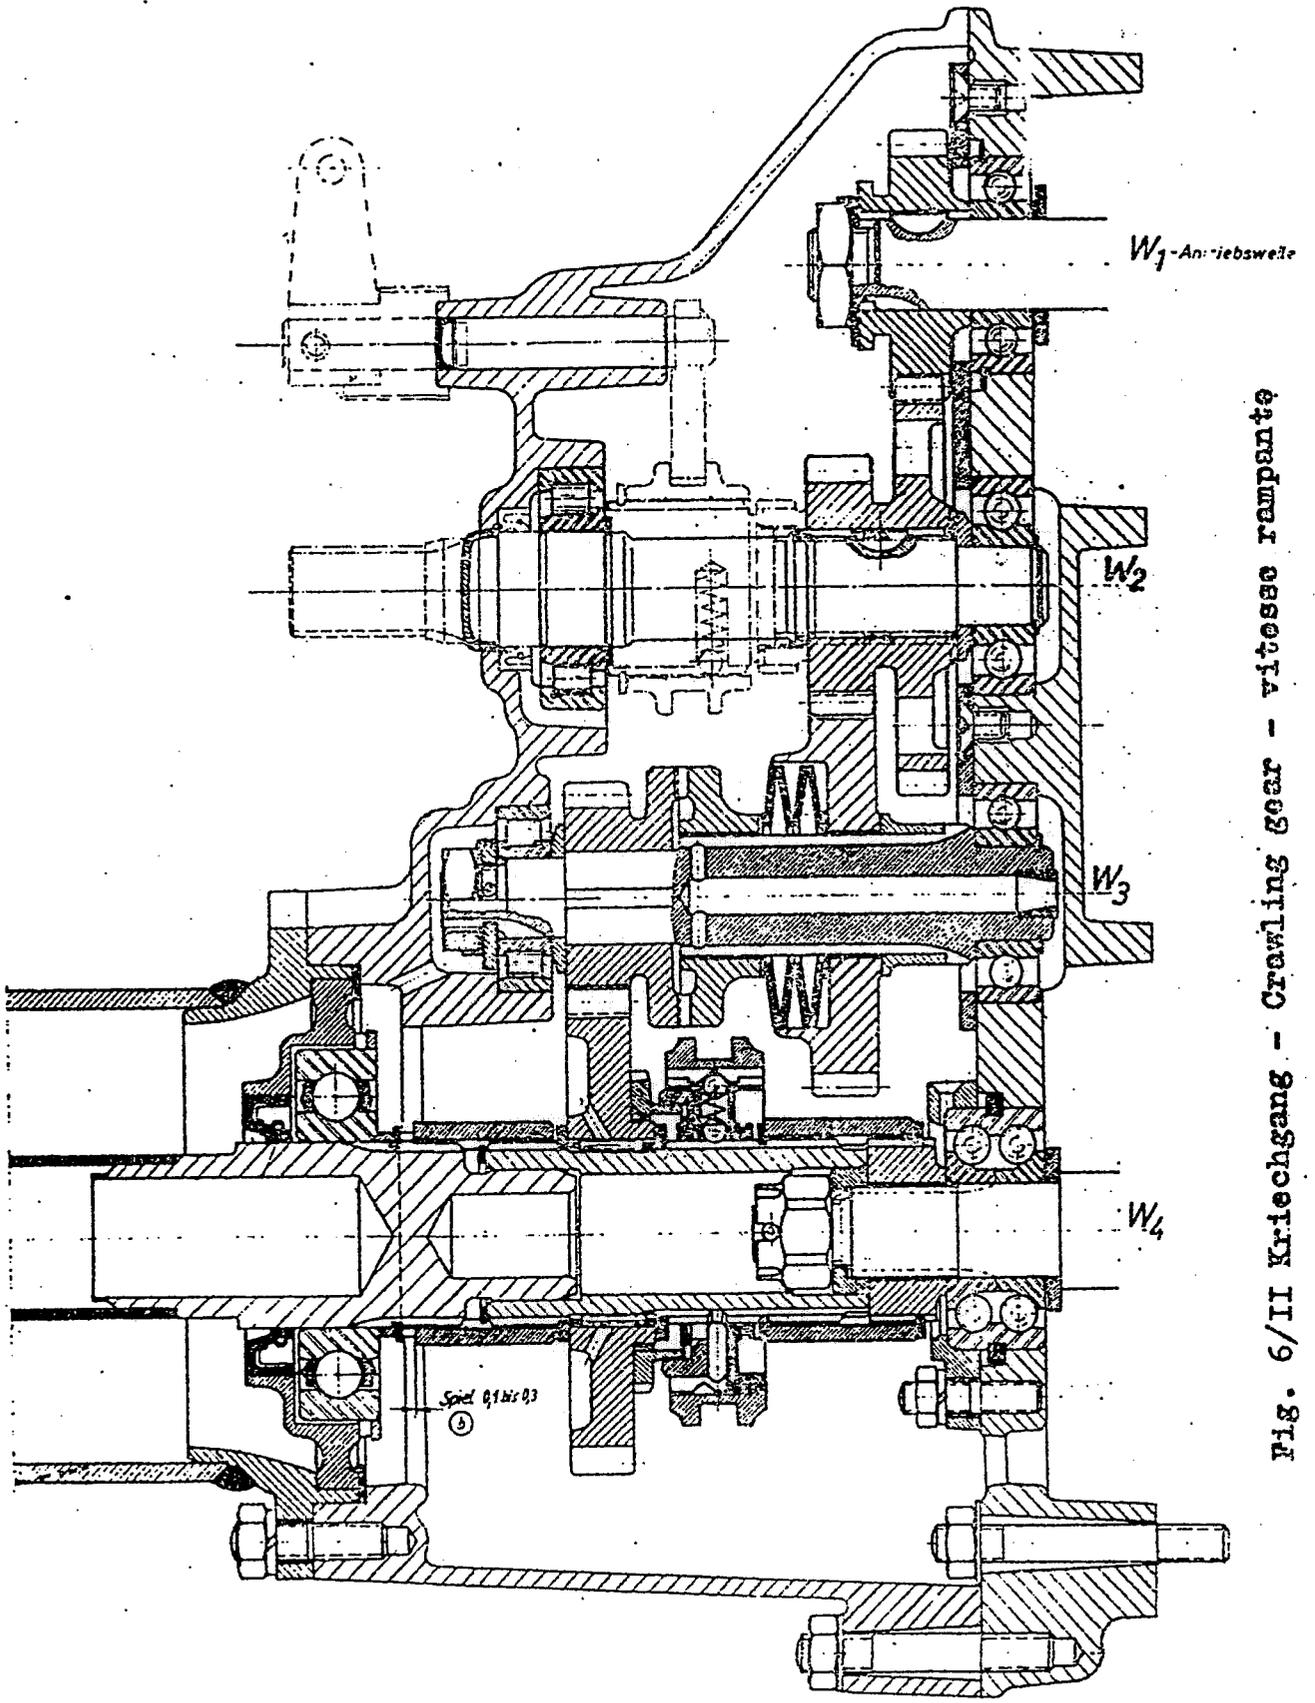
/II Kriechgang - Crawling gear - vitesse rampante
